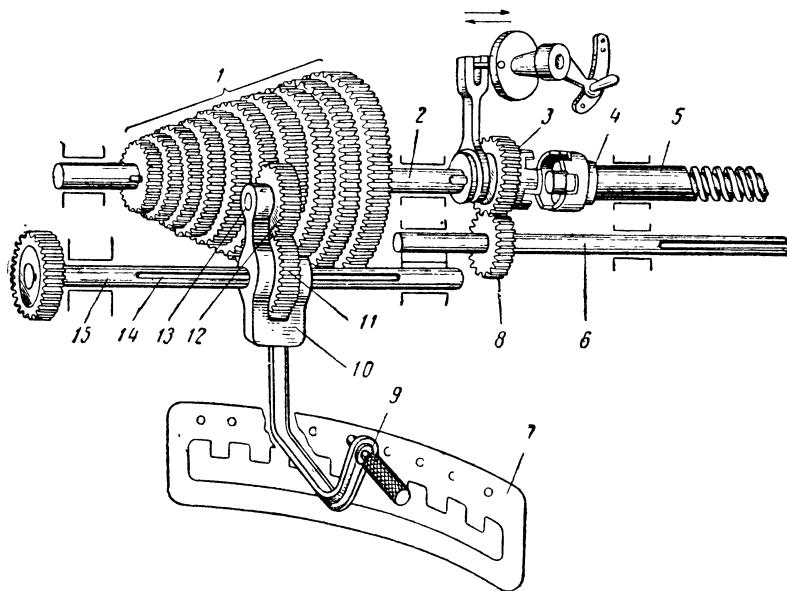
Схема коробки подач с накидным зубчатым колесом
